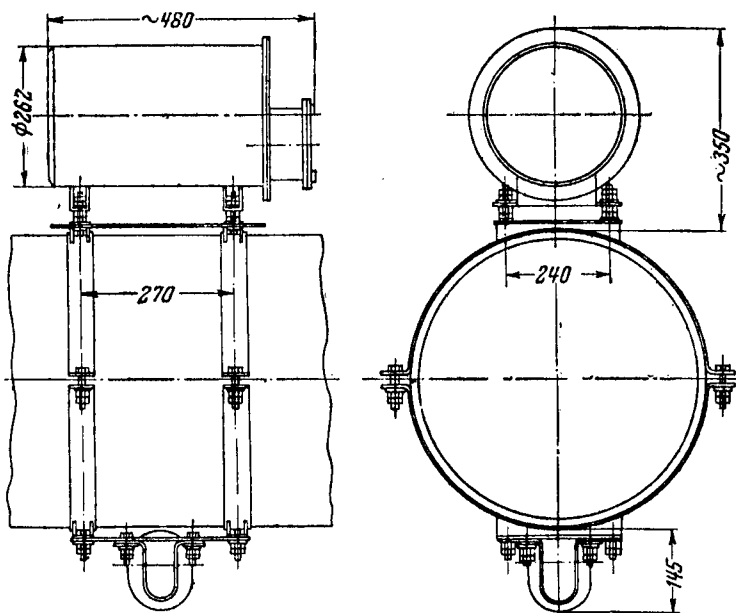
Схема крепления контейнера и камеры на грунтопроводе.
